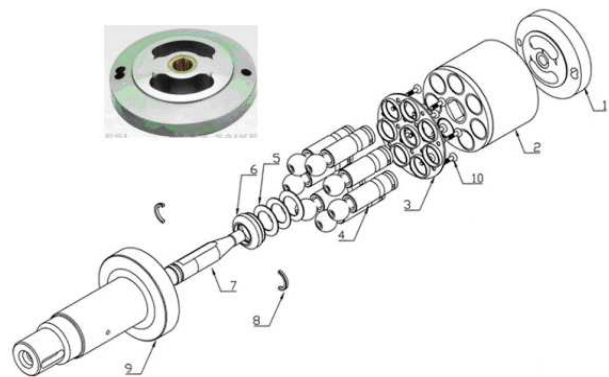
АПГ с СТР: 1 – распределитель; 2 – блок цилиндров; 3 – прижимная пластина; 4 – поршень; 5 – тарельчатая пружина; 6 – держатель тарельчатой пружины; 7 – центральный шип; 8 – сухарь; 9 – ведущий вал; 10 – крепеж пластины
